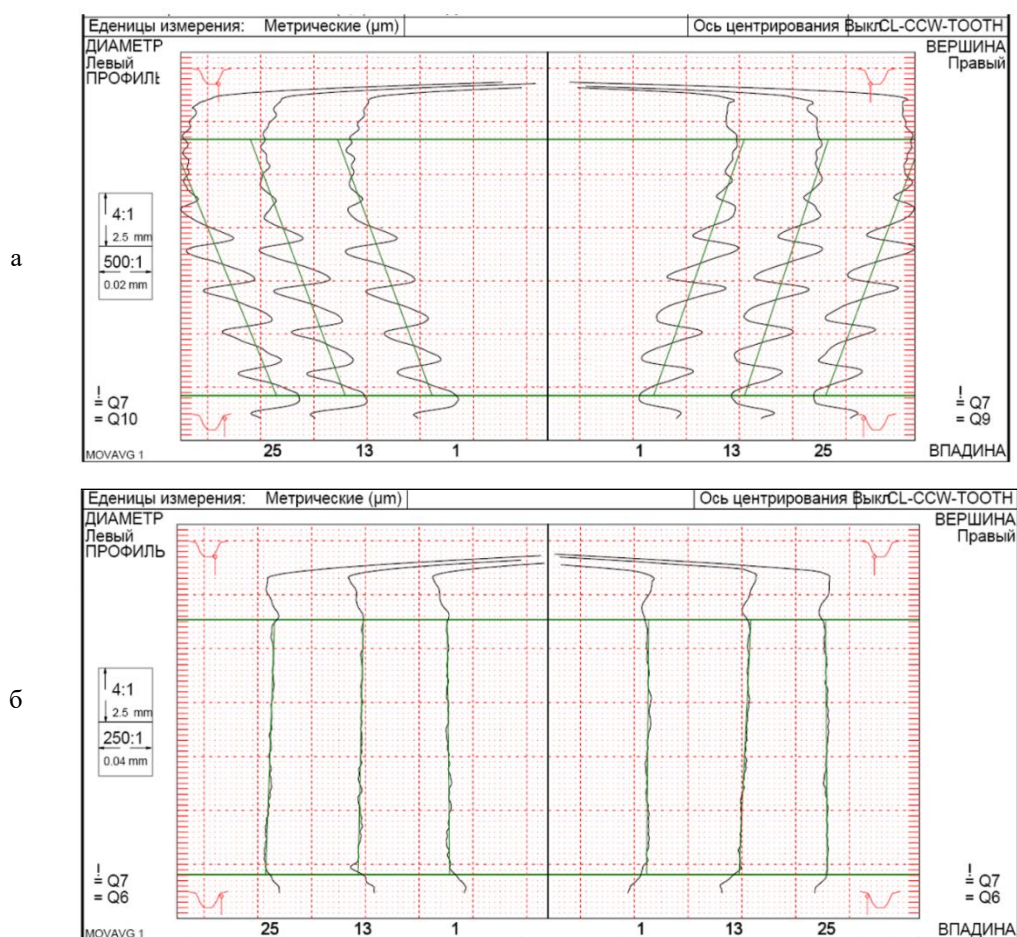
Профилограммы эвольвентного профиля косозубых цилиндрических колес, обработанных при перемещениях дисковой фрезы: а – продольном; б – поперечном
